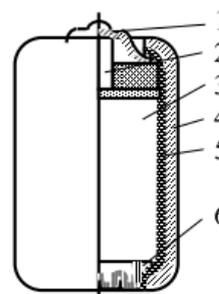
Модернизированный солевой МЦ элемент: 1-крышка; 2-токоотвод; 3-элемент; 4-корпус; 5-гильза; 6-дно
